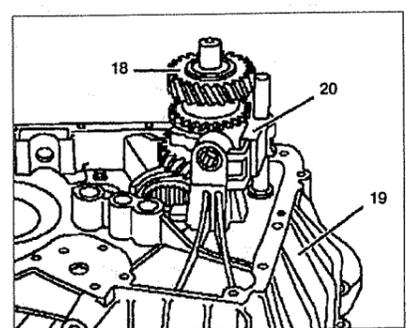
Разборка и сборка коробки передач (автомобили с двигателем 611.980):
